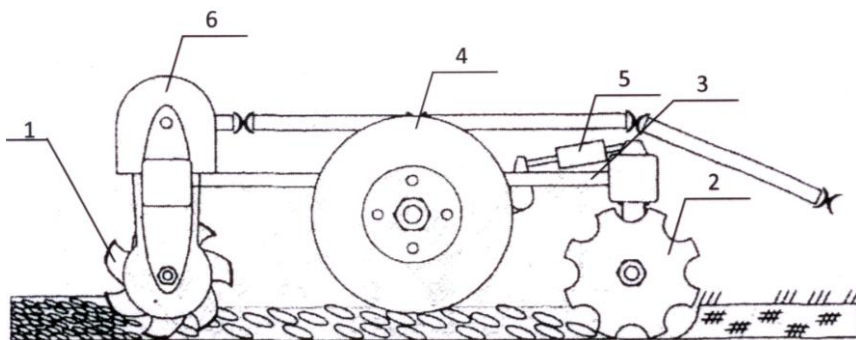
Комбинированный агрегат для подготовки почвы под посев с сферическими дисками и фрезой:
